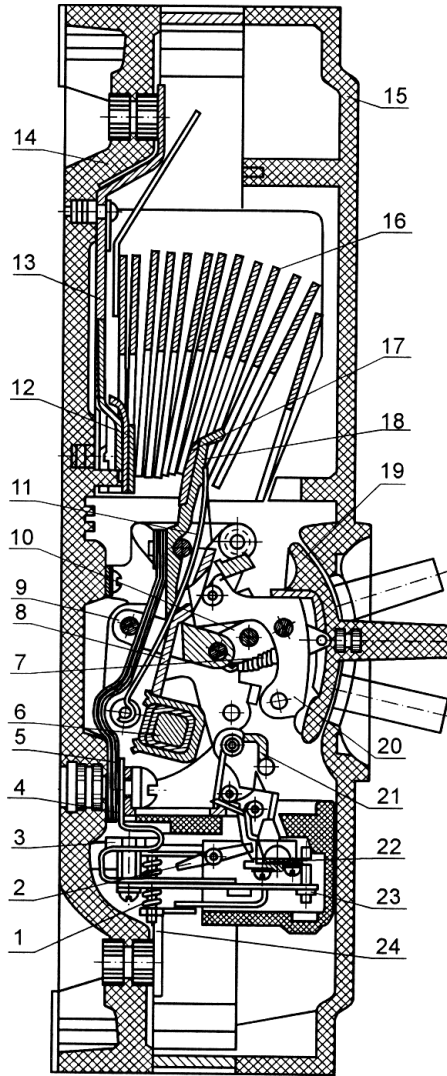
Устройство автоматического выключателя АЗ100: 1 — возвратная пружина; 2 — якорь; 3 — сердечник; 4 — токопровод; 5 — гибкий токопровод; 6 — траверса; 7 — пружина; 8 — контактодержатель; 9 и 10 — рычаги; 11 — плоская пружина; 12 — неподвижный контакт; 13 — основание контакта; 14 — основание; 15 — крышка; 16 — пластины дугогасительной камеры; 17 — подвижный контакт; 18 — основание подвижного контакта; 19 — рукоятка; 20 — рычаг; 21 — собачка расцепителя; 22 — отключающая рейка; 23 — биметаллическая пластинка; 24 — токопровод
